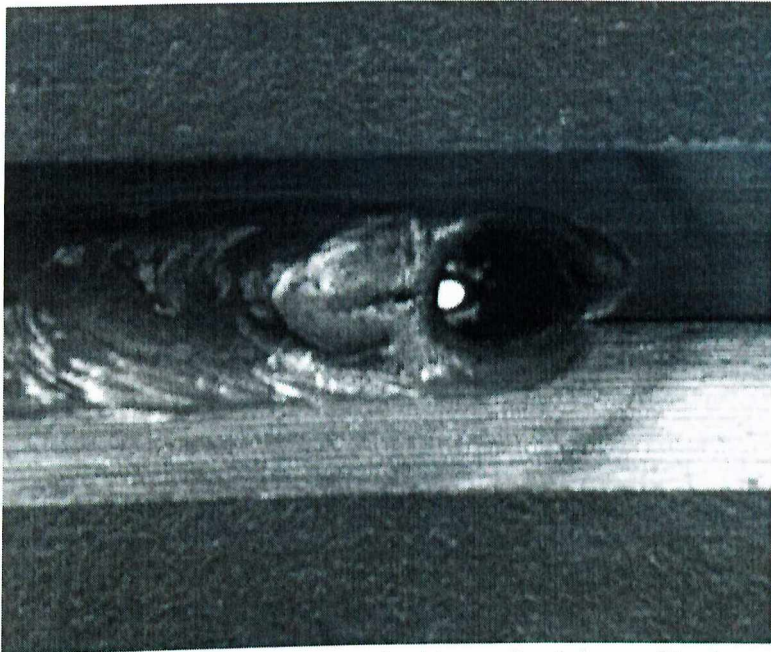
Vista superior do “keyhole” produzido no final do cordão de solda.
